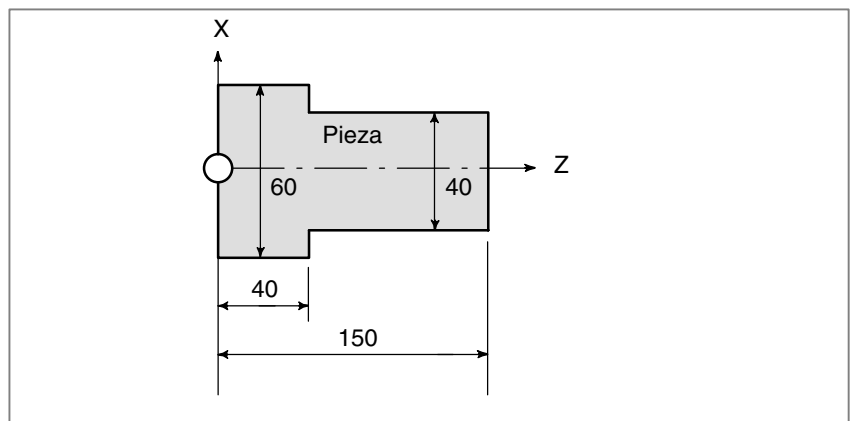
(c) Coordenadas y dimensiones en el plano de la pieza
